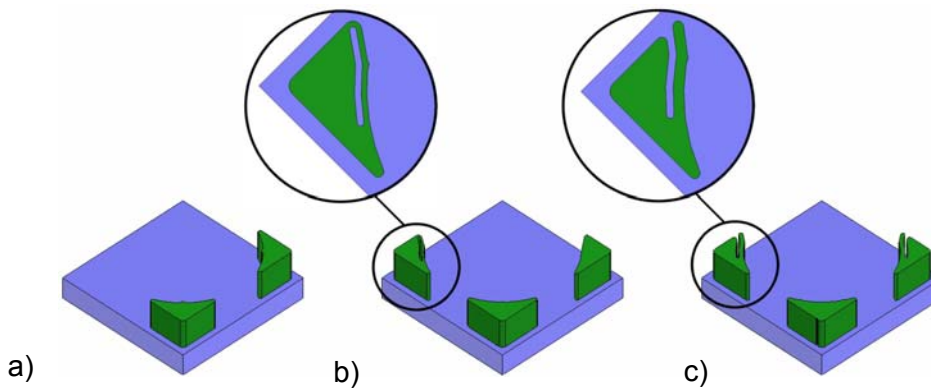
LIGA-Justagestrukturen mit a) Zweipunkt-, b) Dreipunkthalterung mit einem geschlossen Klemmarm und c) Vierpunkt-Halterung mit offenen Klemmarmen
